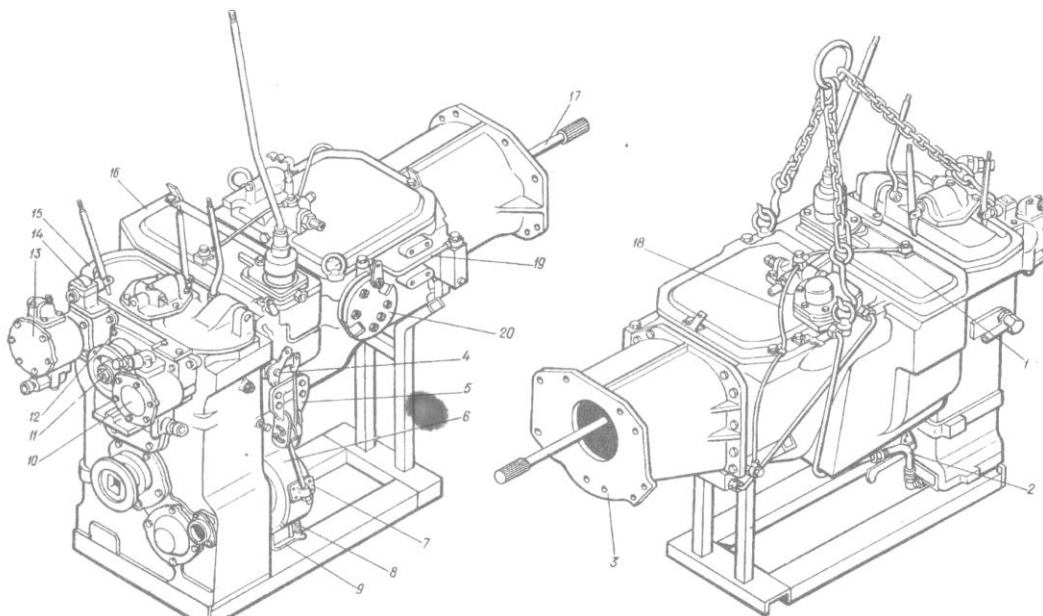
Зняття проставочного корпусу, кришок, насосів: 1, 2, 18 — трубопровід; 3 — корпус проставочний; 4 — вісь; 5, 9 — кронштейн; 6 — барабан; 7 — стрічка; 8 — пружина; 10, 13 —насос; 11 — стакан; 12 — болт; 14 — механізм включення; 15, 16 — кришка; 17 — вал; 19 — трубка; 20 — гідроаккумулятор
